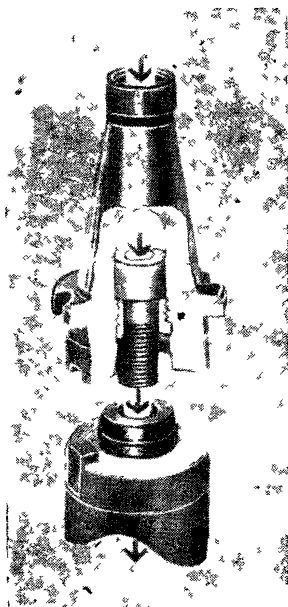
Пример типового конструктивного решения агрегатирования инструмента с внутренним полем СОЖ
